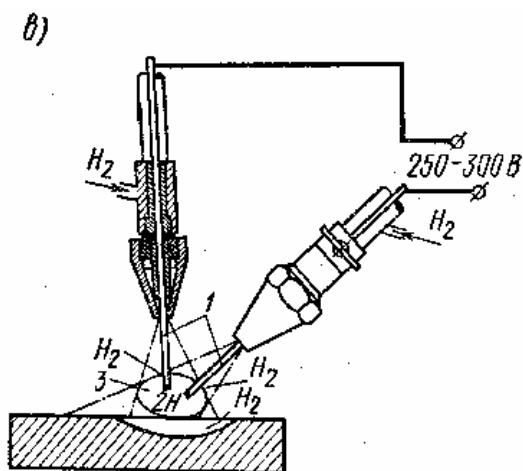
,в Аргоно-дуговая сварка атомноводородная сварка
